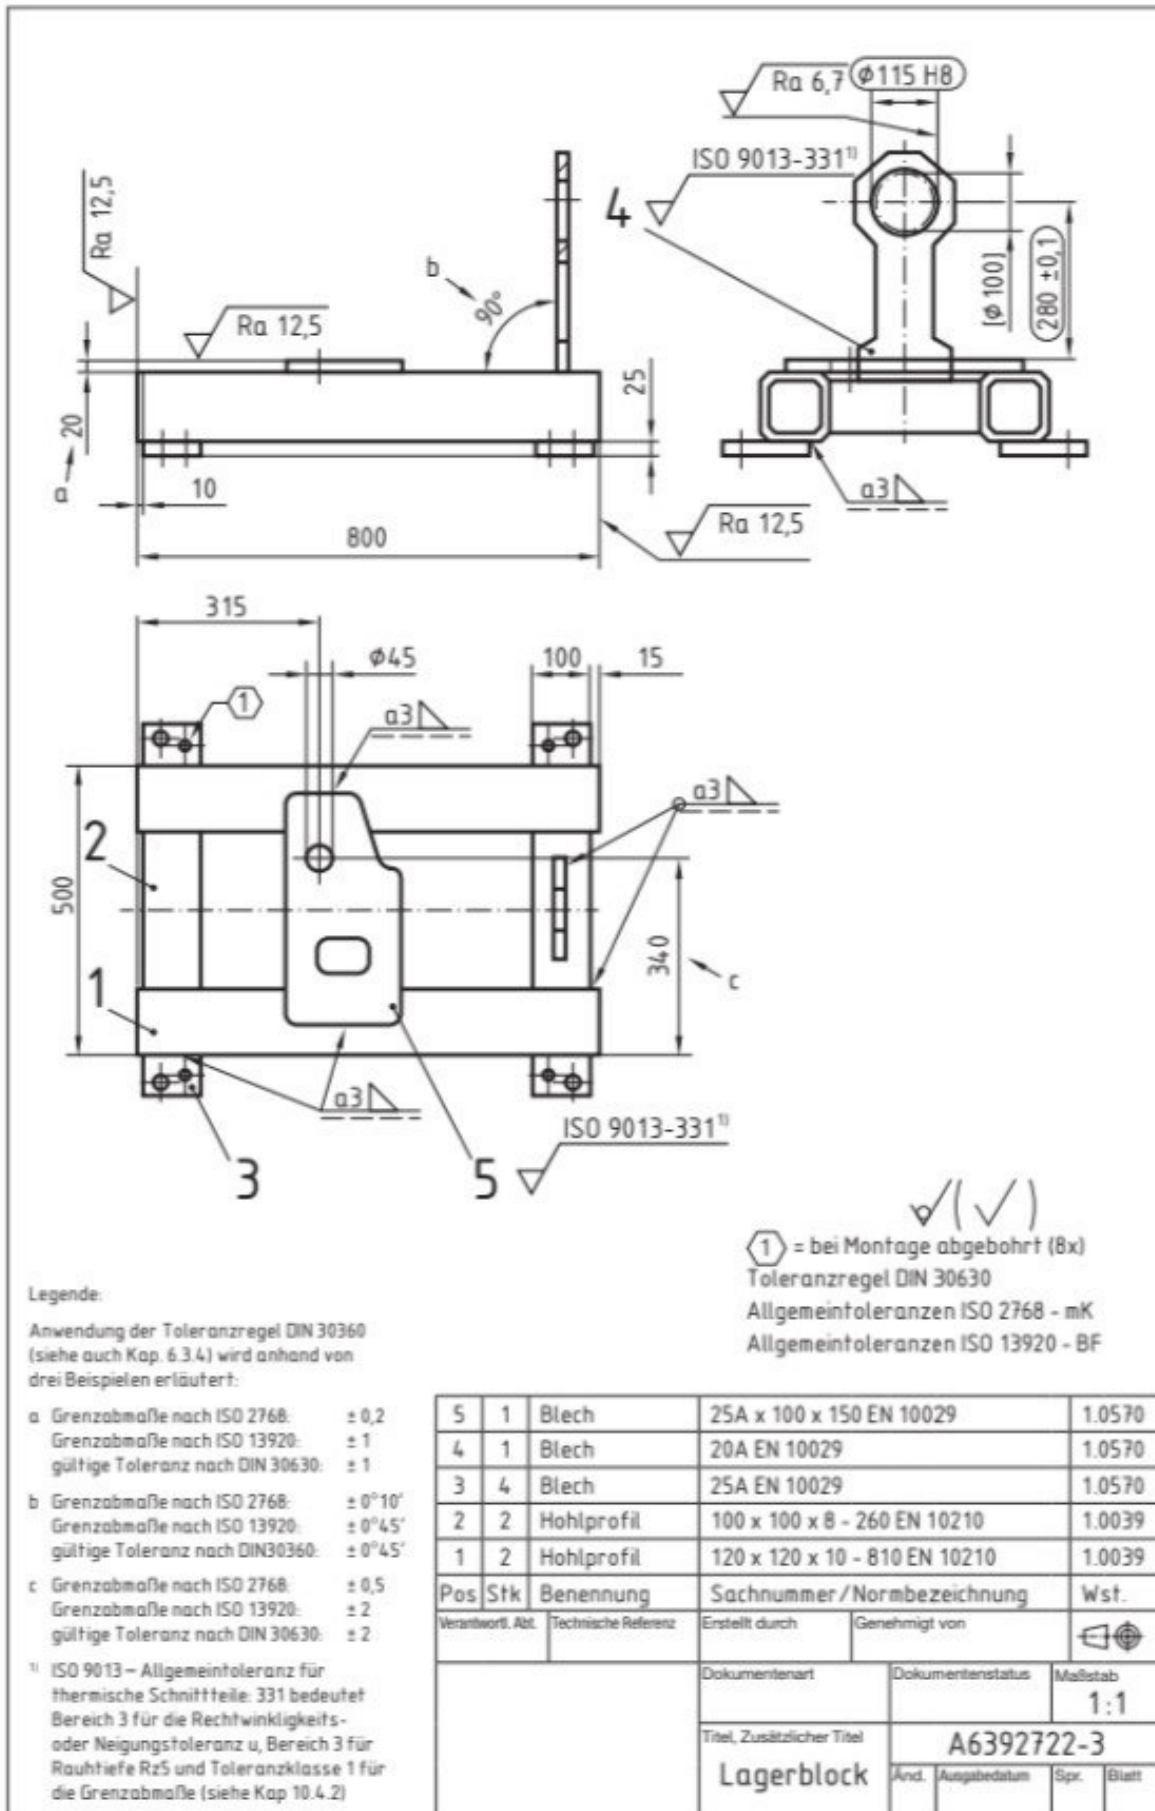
Зварювальний кресленик «Блок зберігання»
